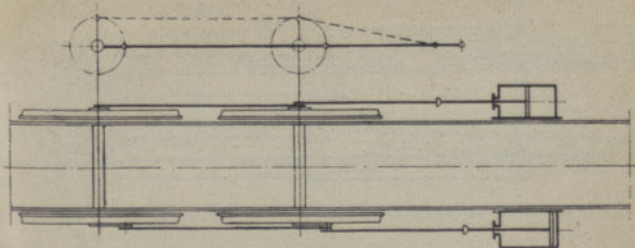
Mechanismo motor para simples expansão, com 2 cylindros exteriores.
